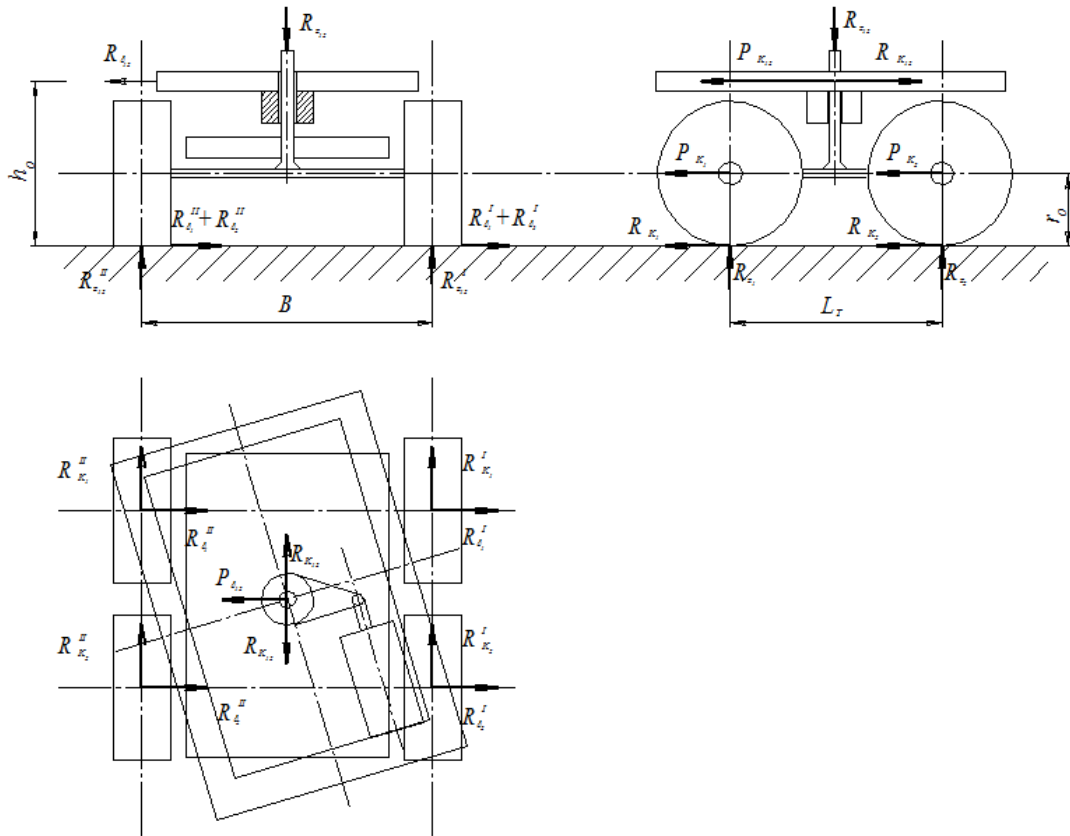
Розрахункова схема для визначення нормальних реакцій дороги на колесах передньої поворотної платформи
